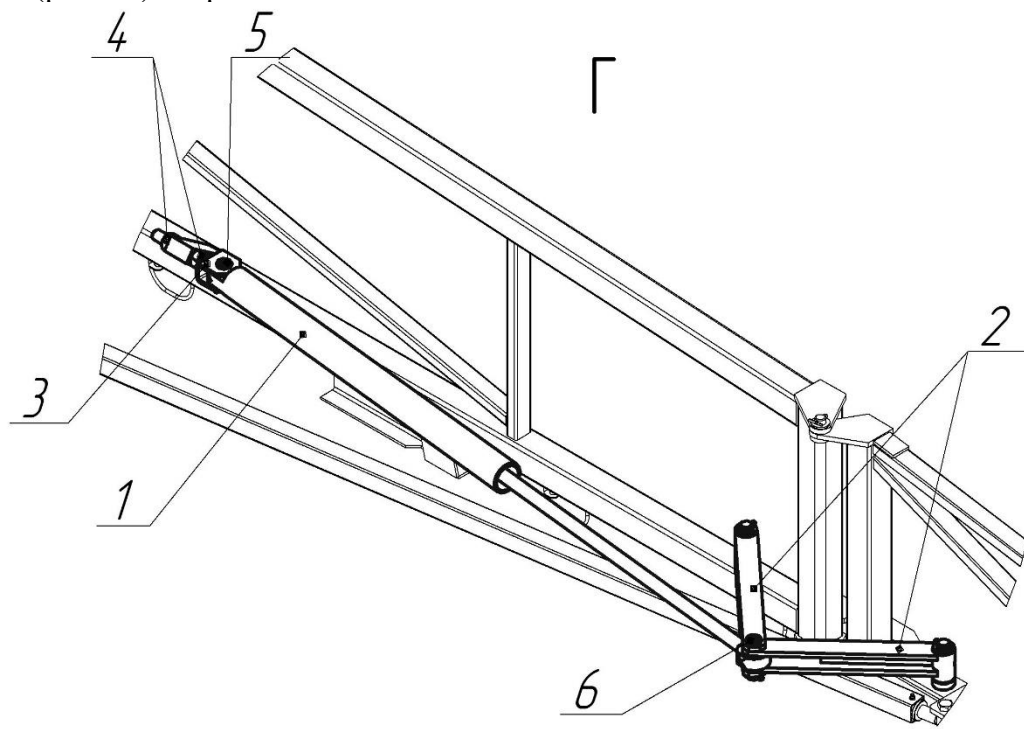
Элементы регулировки гидроцилиндра складывания штанги.
